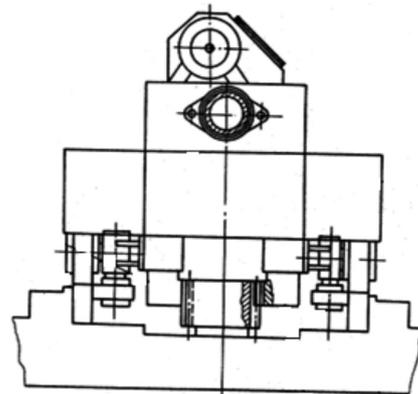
Отрезной станок для резки непрерывно движущихся труб на мерные заготовки
